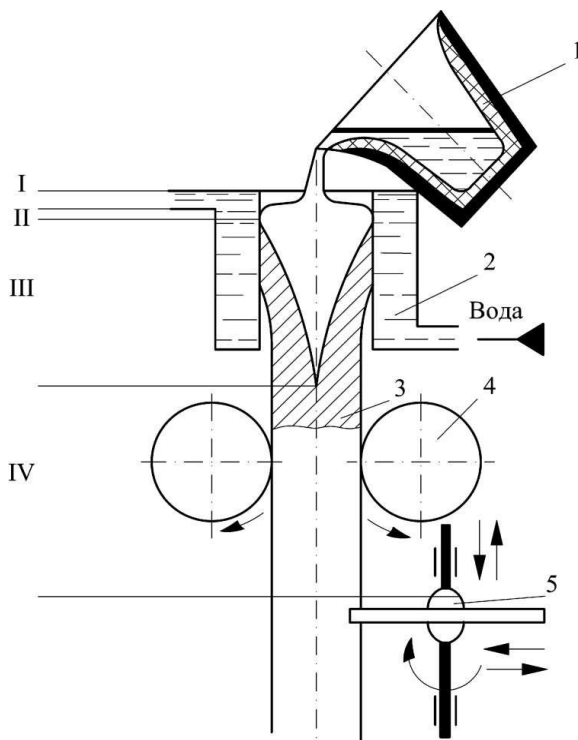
Схема получения отливок при непрерывном литье: 1 - ковш; 2 - кристаллизатор; 3 - затвердевшая часть отливки; 4 - валки; 5 - пила;
